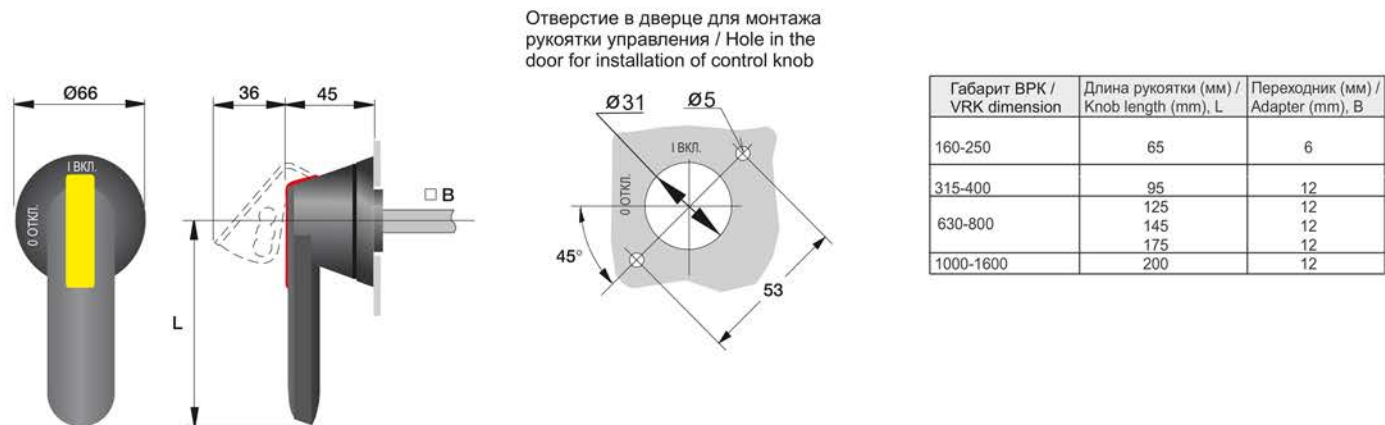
Габаритные размеры рукояток управления / Figure 8 – Overall dimensions of control knobs
